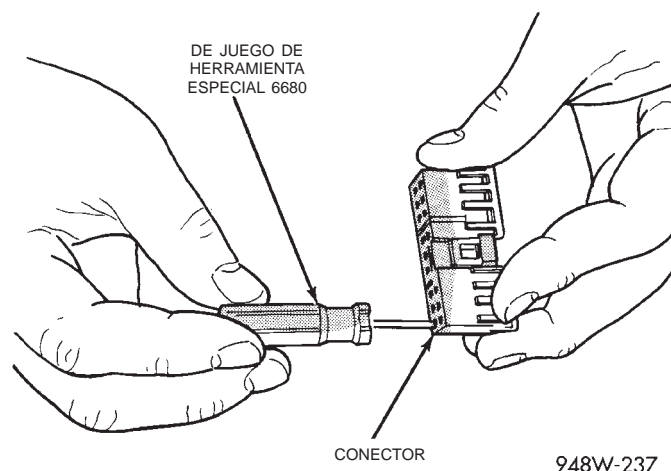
Desmontaje del terminal utilizando la herramienta especial
